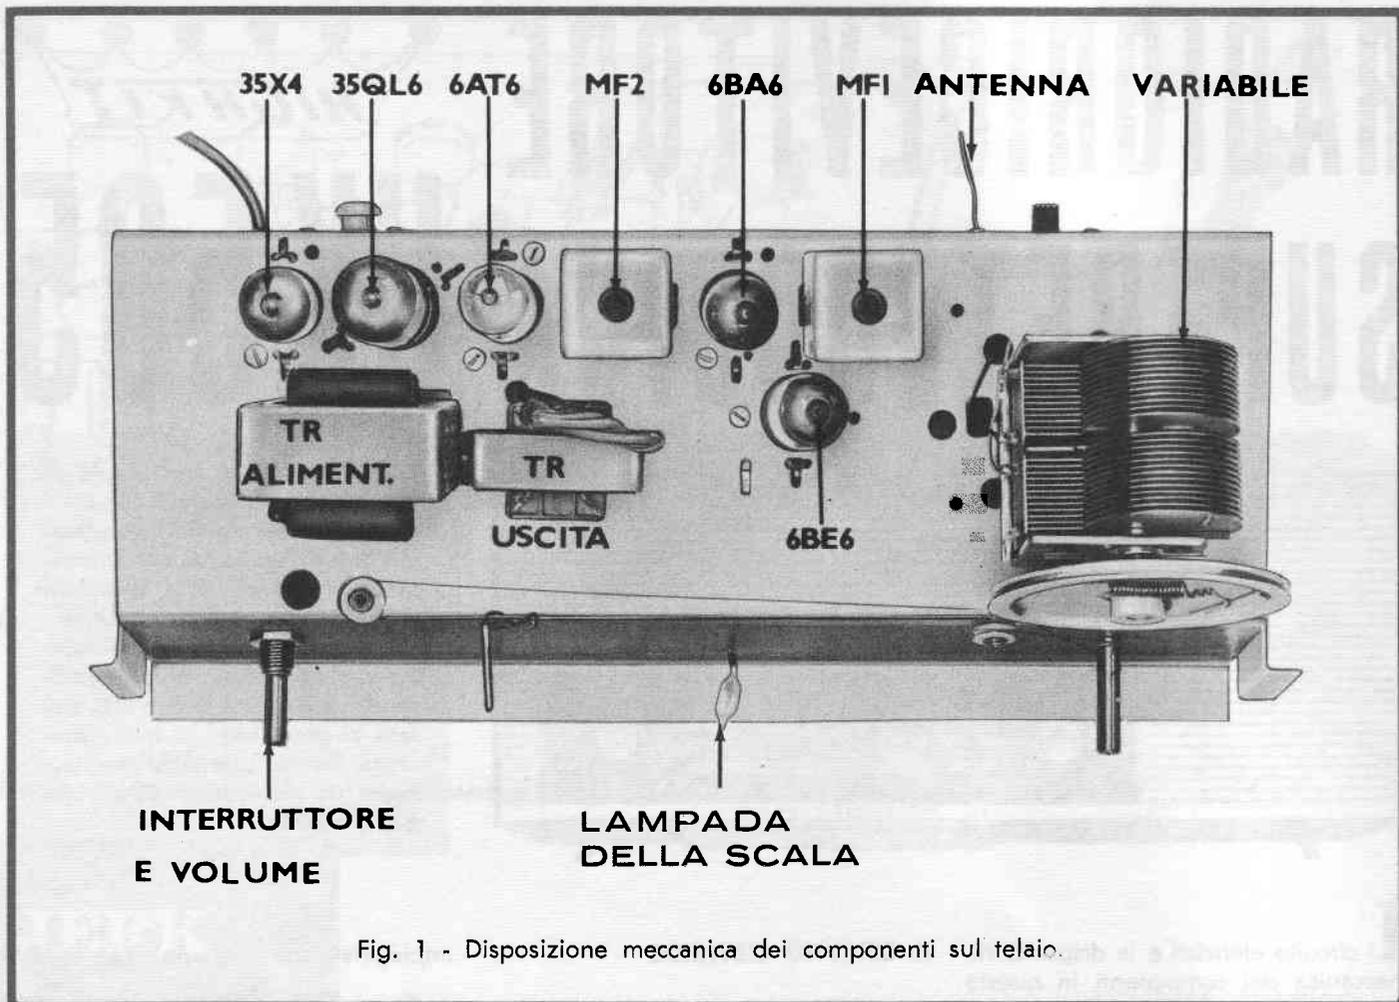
Disposizione meccanica dei componenti sul telaio.
